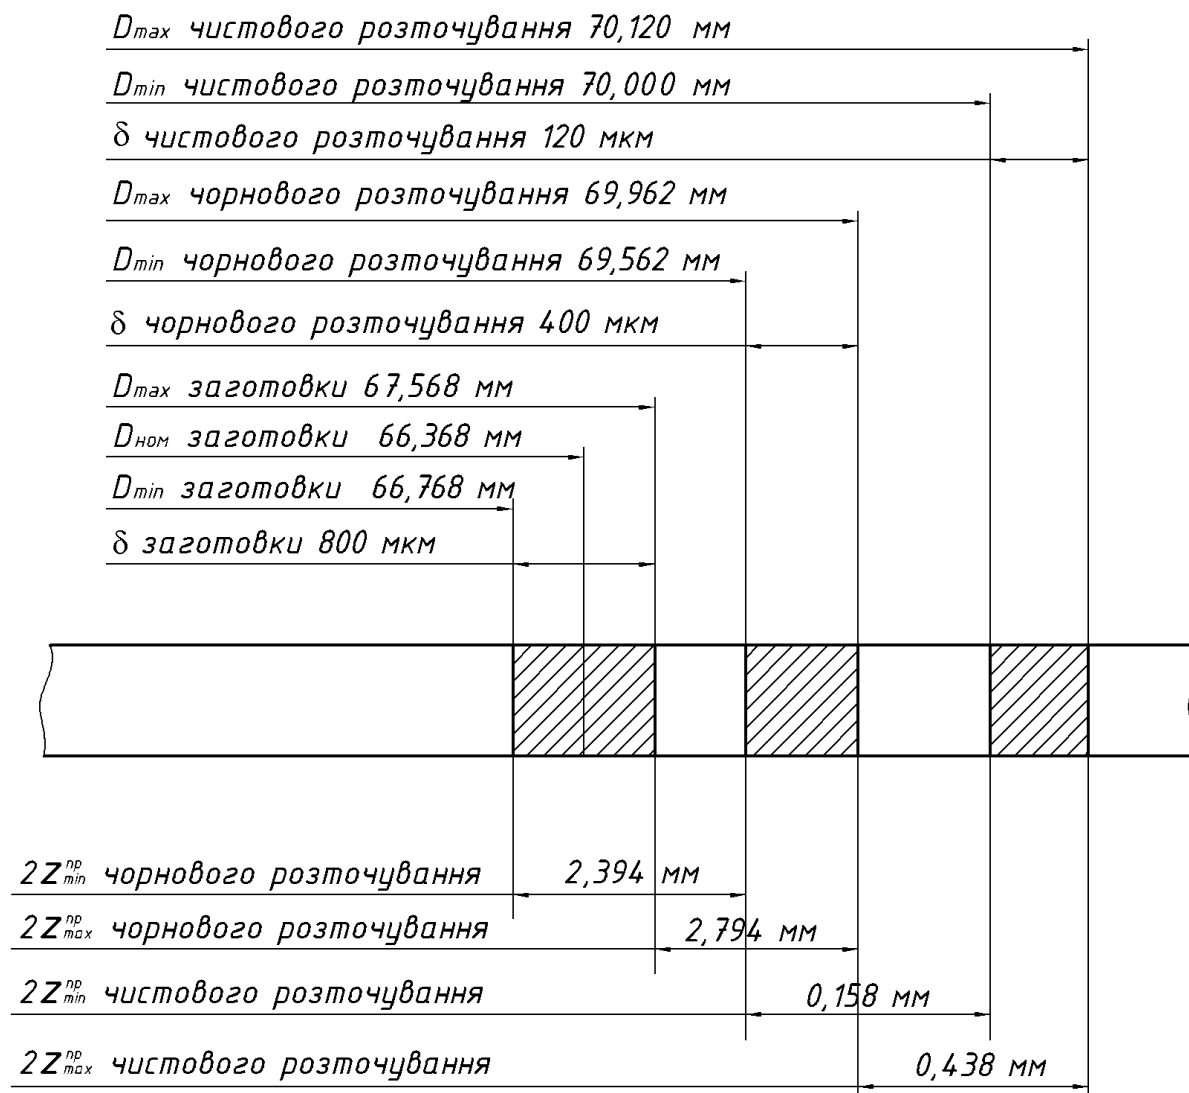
Схема графічного розташування припусків та допусків на оброблення поверхні $\varnothing 70 \text{ H}10^{(+0,120)}$
